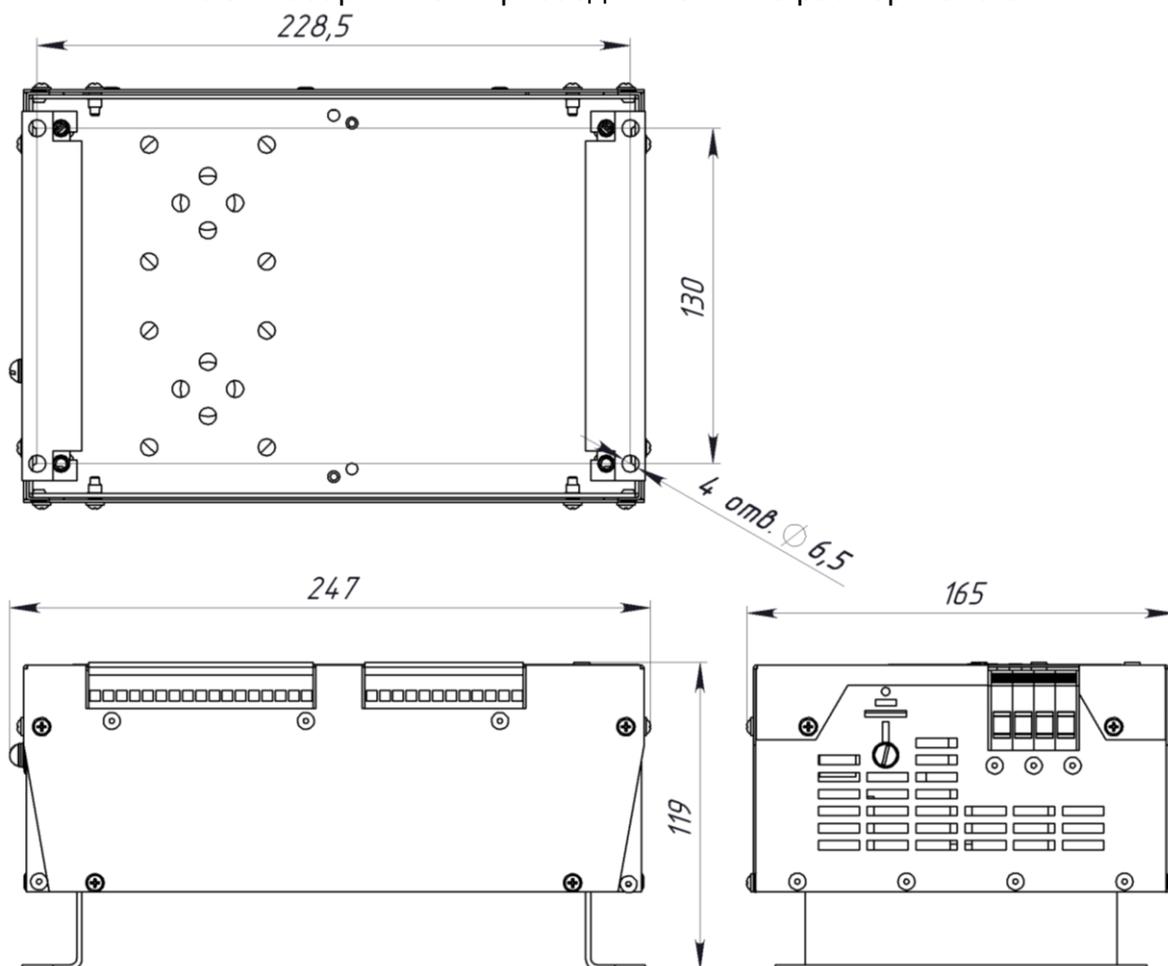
Габаритные и установочные размеры с дополнительными кронштейнами
